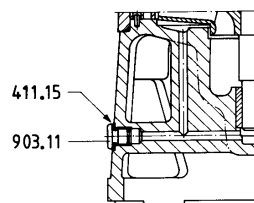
Baugrößen LV 25/32/40, Schmierbohrung für Gleitlager, saugseitig mit Verschlußstopfen
